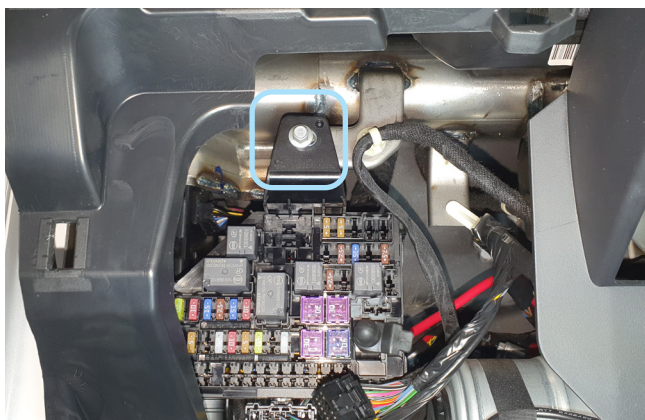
Болт крепления монтажного блока предохранителей сверху
